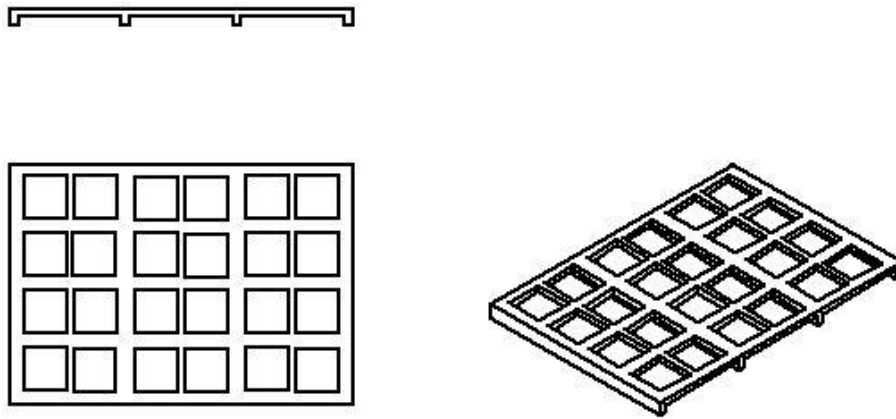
Alzado, planta y vista isométrica de la pieza soporte.
